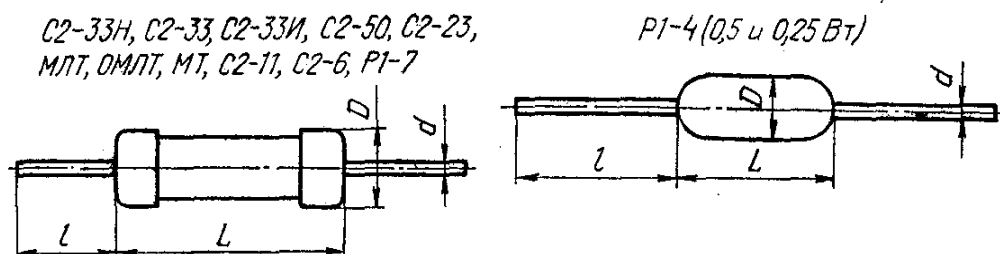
Конструкция и размеры резисторов общего назначения
